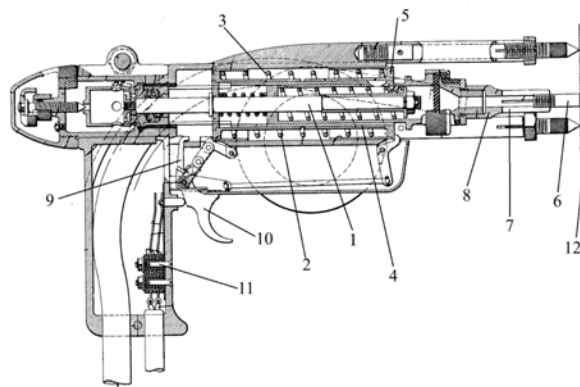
Головні елементи «механізму для стикового зварювання» конструкції Е. Нельсона
